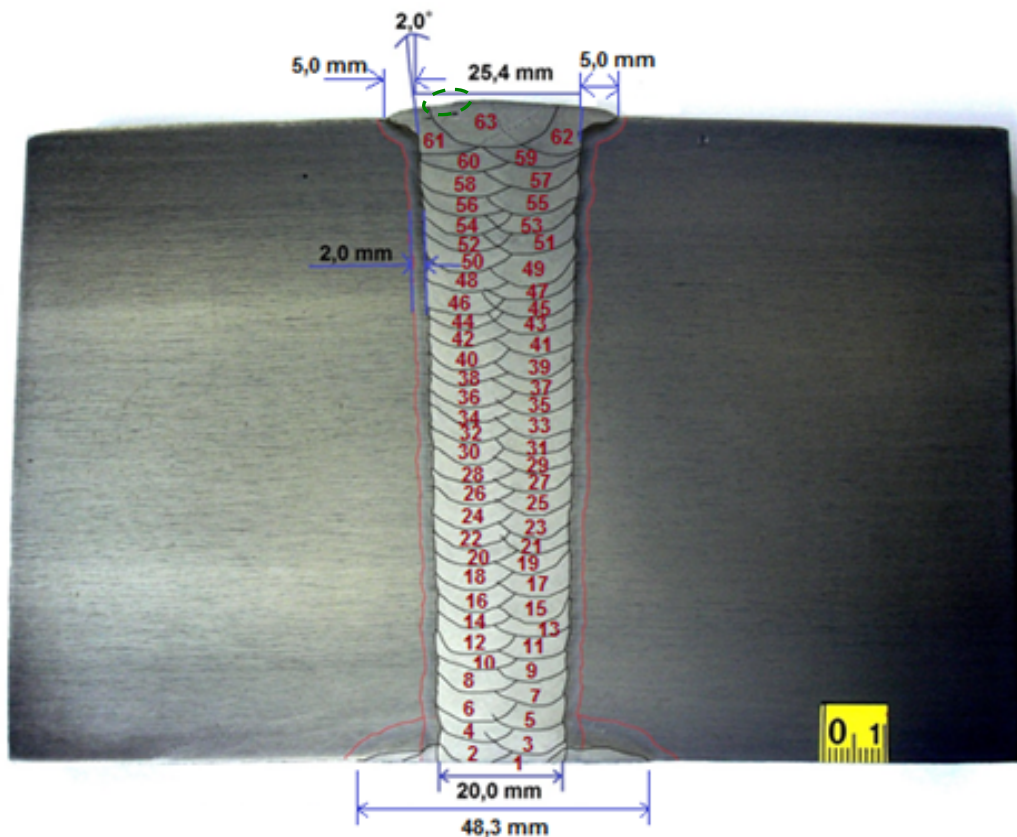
Macrografia da junta soldada do aço 2,25Cr-1Mo-0,25V: dimensões dos passes, da ZAC, do ângulo do chanfro, abertura da raiz, da contrassolda e do passe de revenimento.
